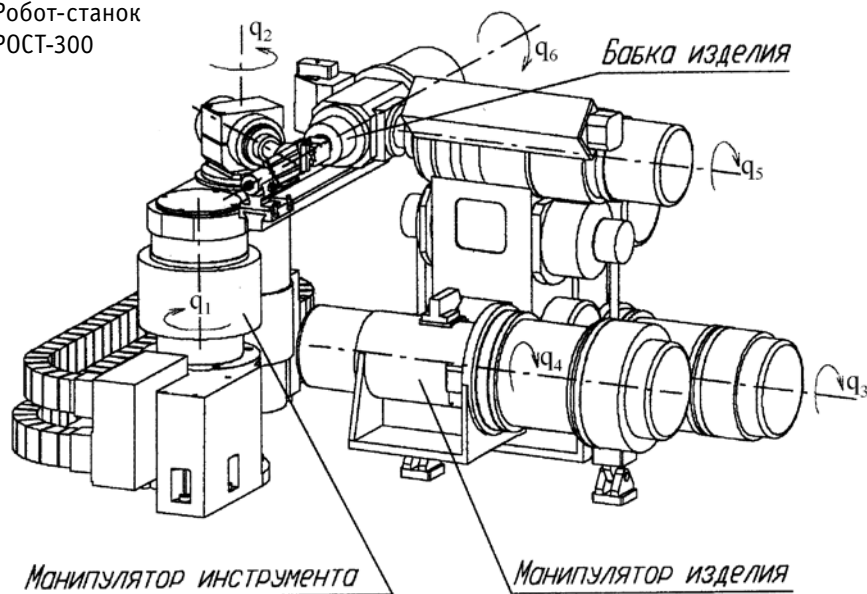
Зуборезный станок с разделением функции воспроизведения относительного движения (заготовки и инструмента)
